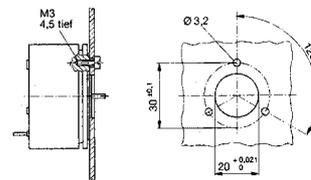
Bohrplan für Befestigung mit 3 Zylinderschrauben M3.
